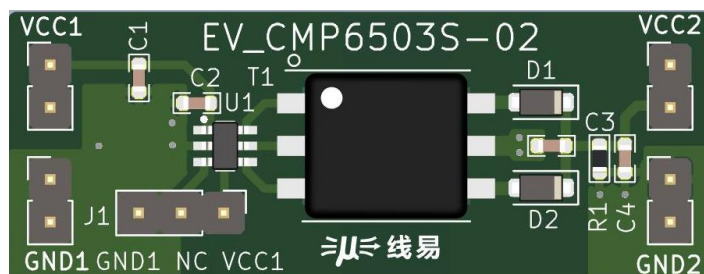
PCB 示意图(尺寸: 16 x 42mm)
